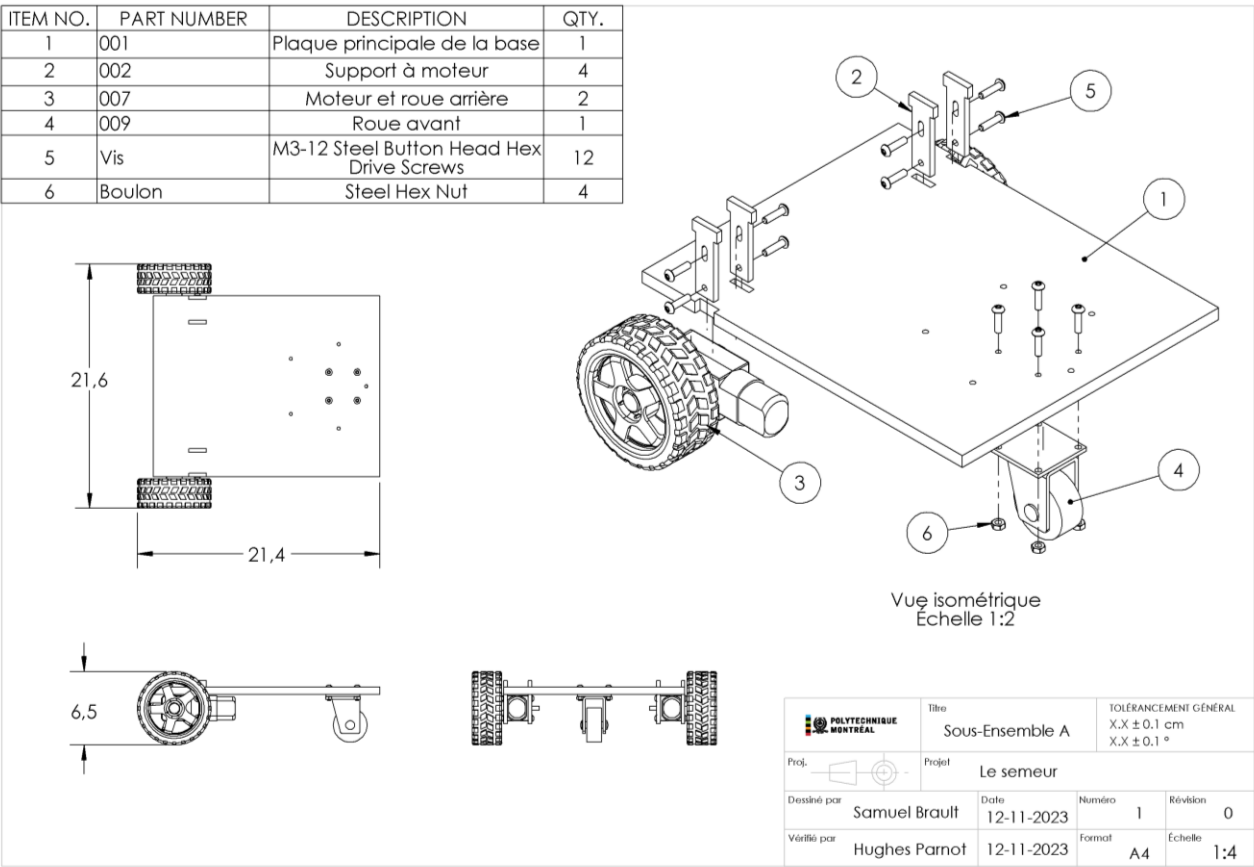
Dessin d'assemblage du Sous-Ensemble A
